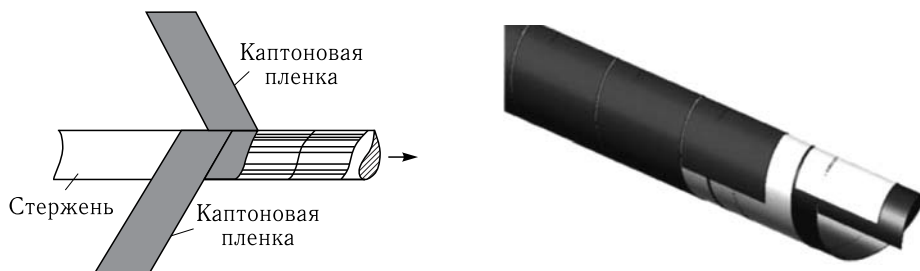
Слева: схема процесса намотки строу-трубки на калиброванный стержень. Справа: схема конструкции строу. Из [60, 62]
